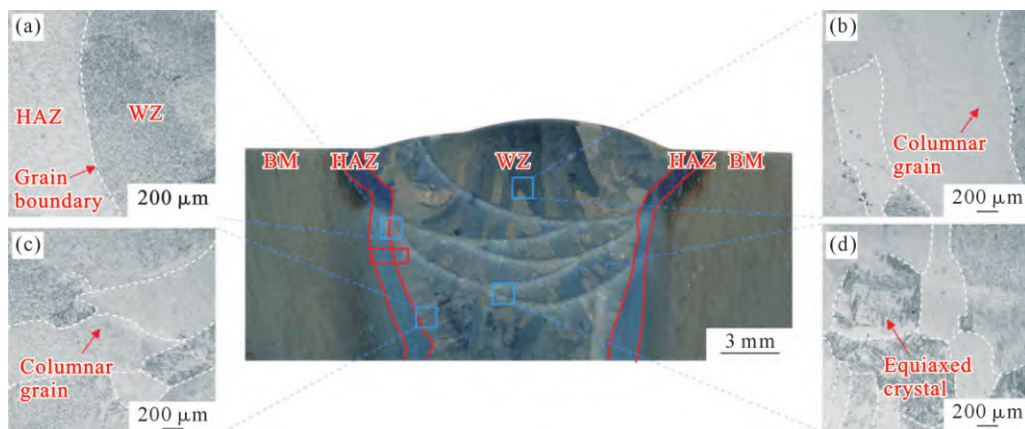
焊缝金相组织:(a) 热影响区与焊缝边缘;(b) 焊缝边缘;(c) 焊缝中央;(d) 焊缝底部
